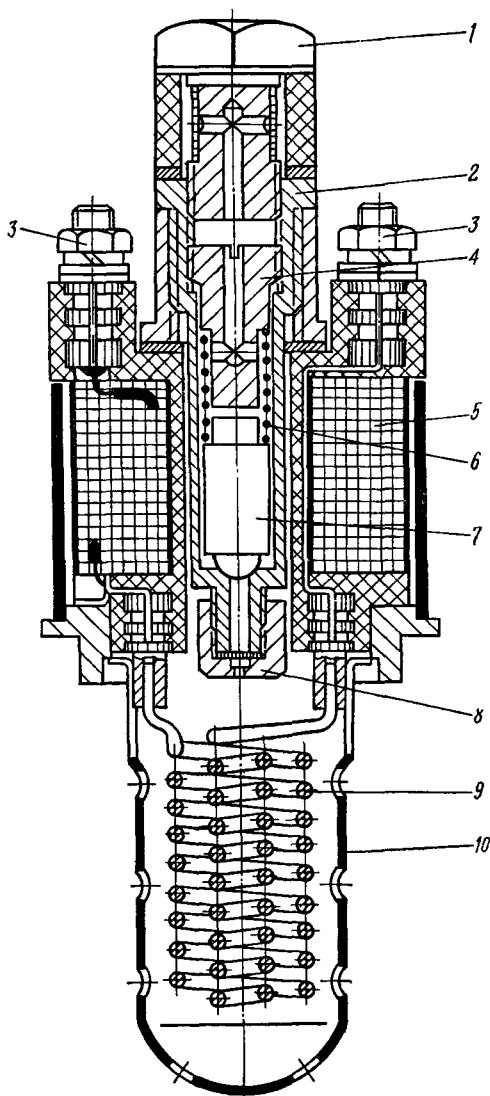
Предпусковой электрофакельный подогреватель воздуха:
